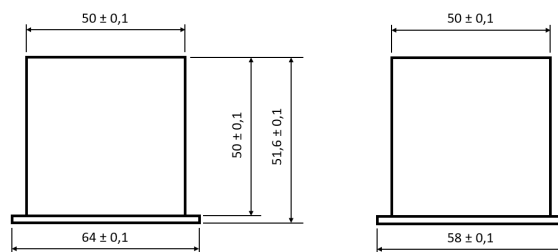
PocketQube Geometrie - die Maße sind in Millimetern gegeben
